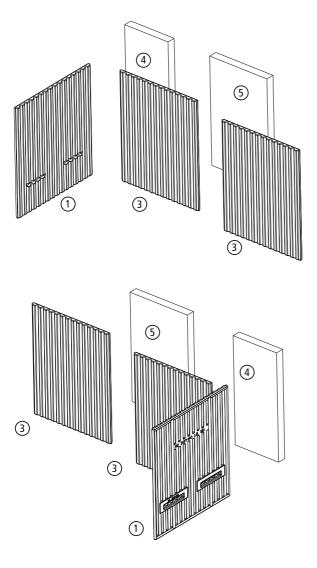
Revêtement de la chambre de combustion FINA ES
